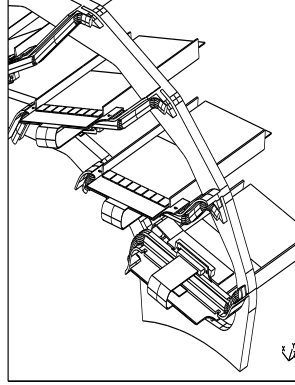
Dettaglio di montaggio di un modulo nella ruota.
